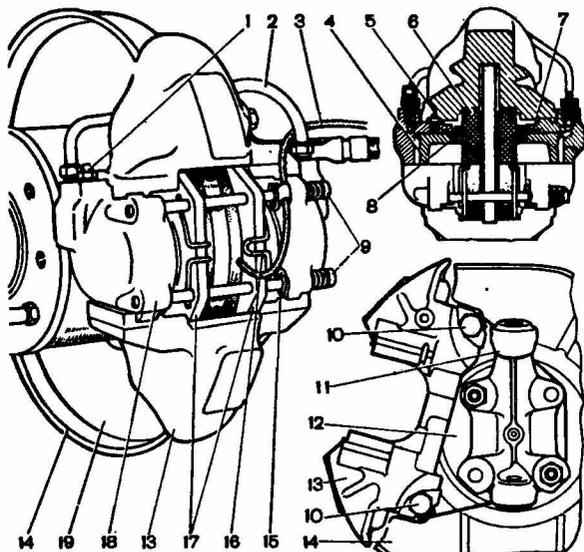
Тормозной механизм переднего колеса: 1 - штуцер для прокачки привода передних тормозов; 2 - соединительная трубка рабочих цилиндров; 3 - провод сигнализатора износа накладок тормозных колодок; 4 - поршень колесного цилиндра; 5 - фиксатор колесного цилиндра; 6 - накладка тормозной колодки; 7 - уплотнительное кольцо; 8 - пылезащитный колпачок; 9 - пальцы крепления колодок; 10 - болт крепления суппорта к кронштейну; 11 - поворотный кулак; 12 - кронштейн крепления суппорта; 13 - суппорт; 14 - защитный кожух; 15 - шплинт; 16 - прижимная пружина колодки; 17 - тормозные колодки; 18 - колесный цилиндр; 19 - тормозной диск
